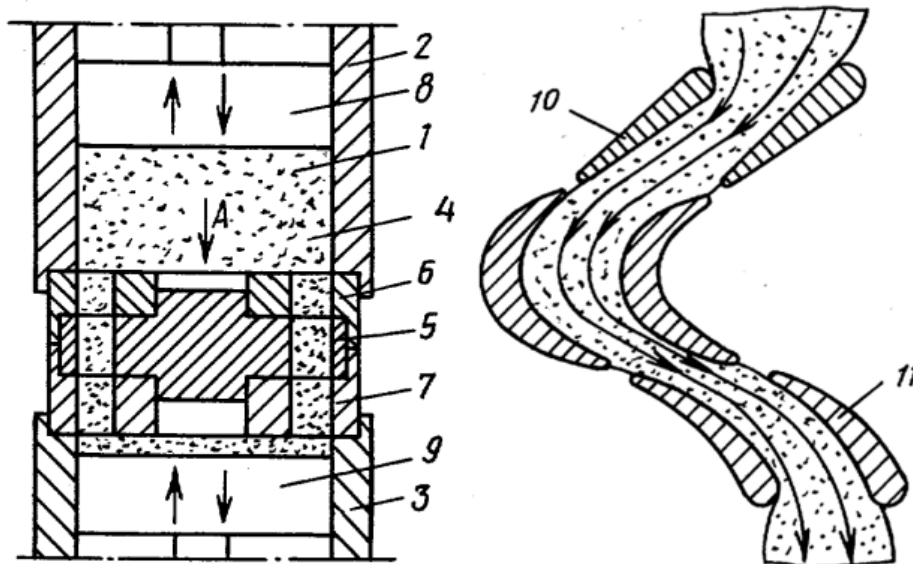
Способ обработки деталей абразивной массой [8]
